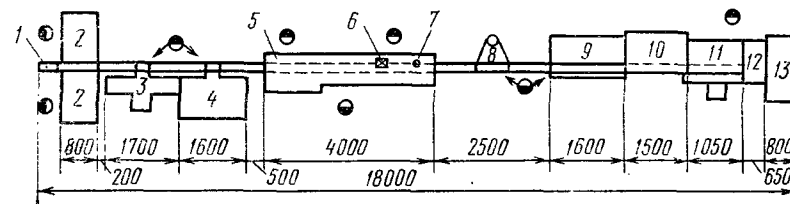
Схема механизированной линии сборки тяговых аккумуляторов со сварным блоком пластин:
